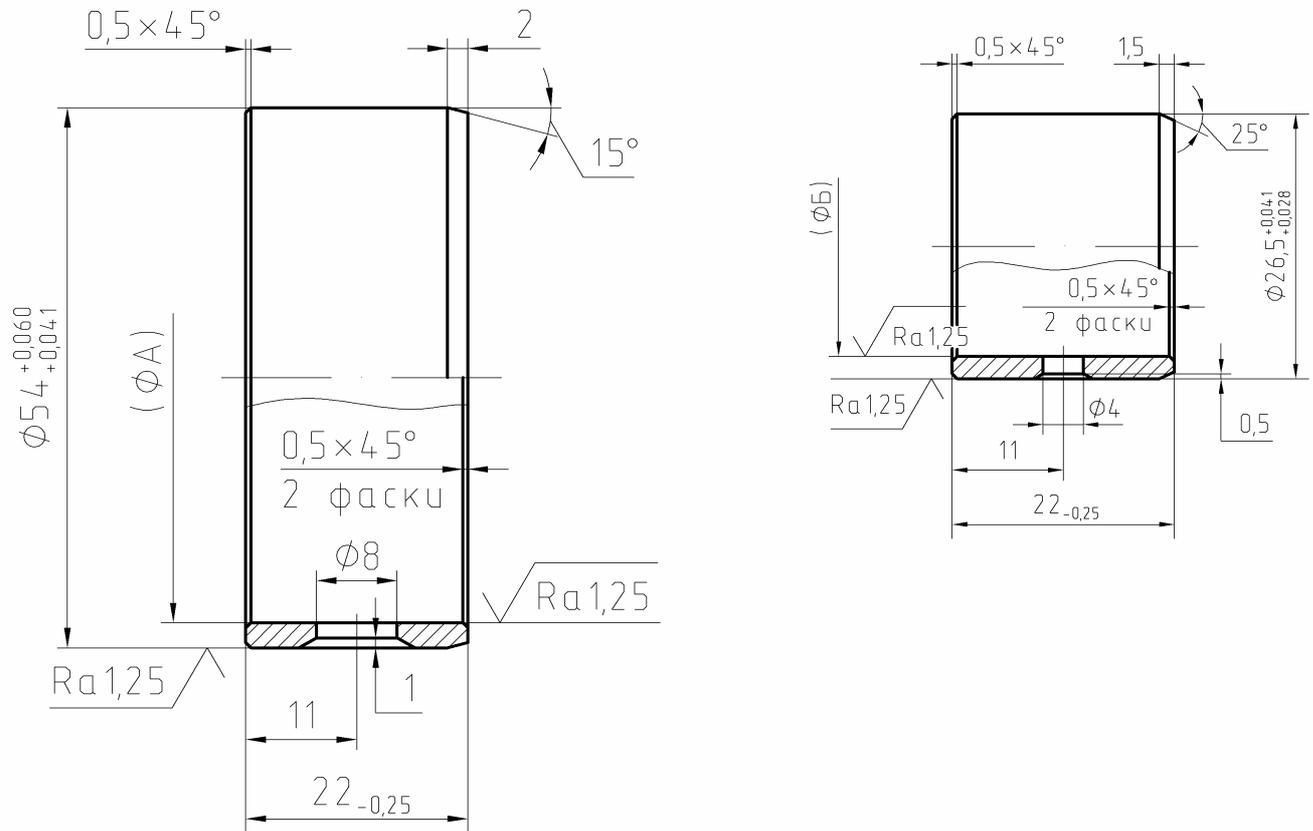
Ремонтные втулки опор промежуточного вала
